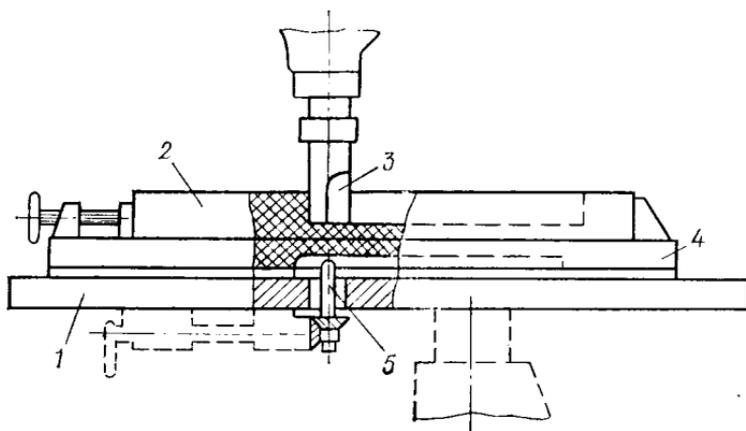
Схема фрезерования на копировально-фрезерном станке
